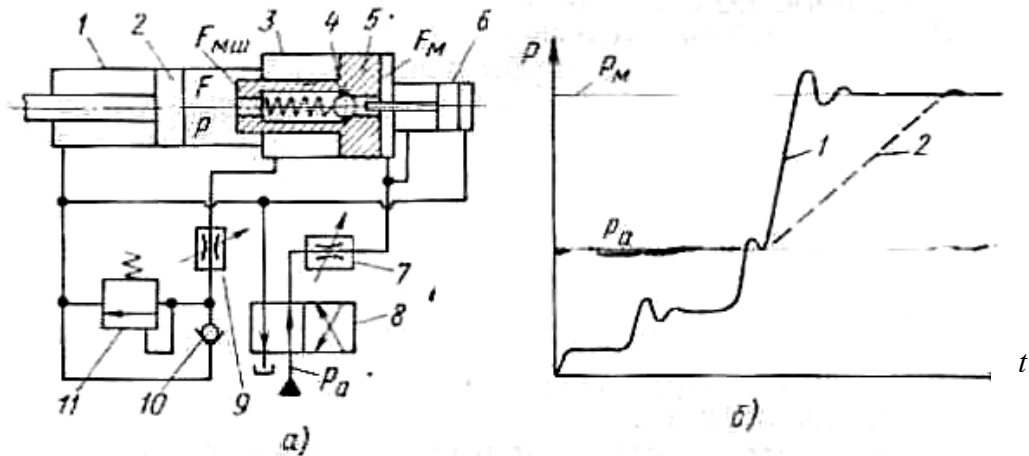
Гидропривод с мультипликатором механизма прессования машины литья под давлением
